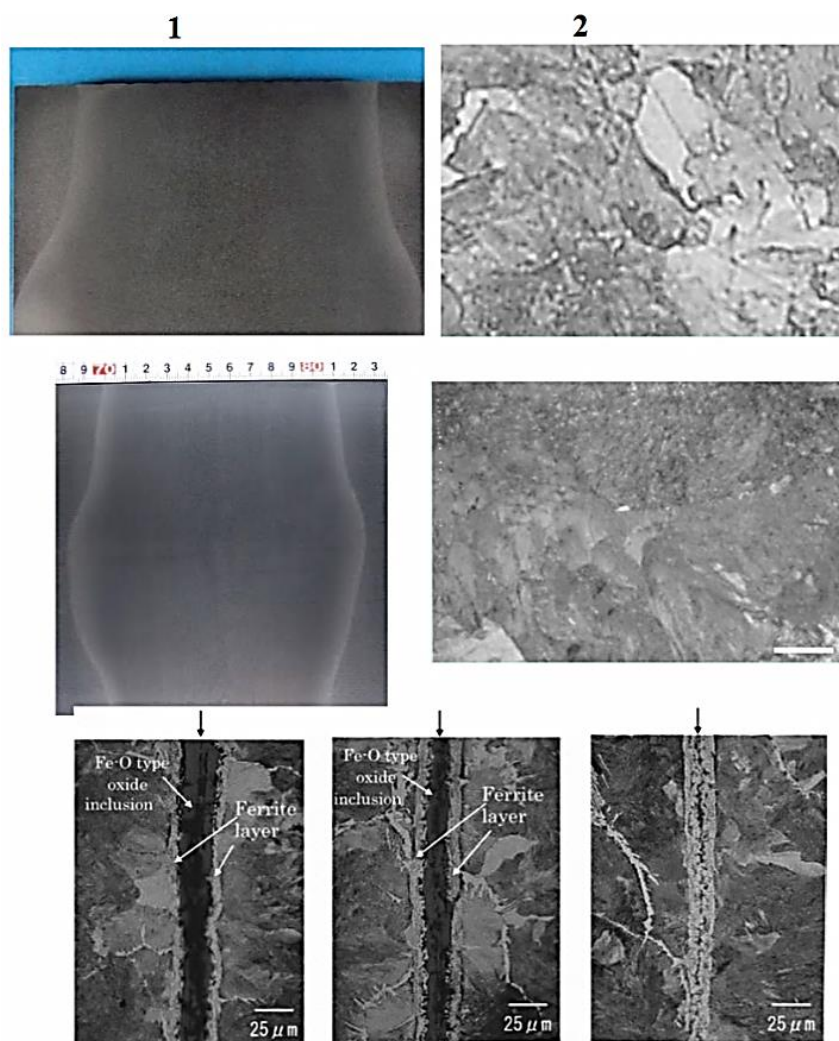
Макро- и микроструктура сварного стыка после газопрессовой сварки и неметаллические включения в зоне сварного шва
